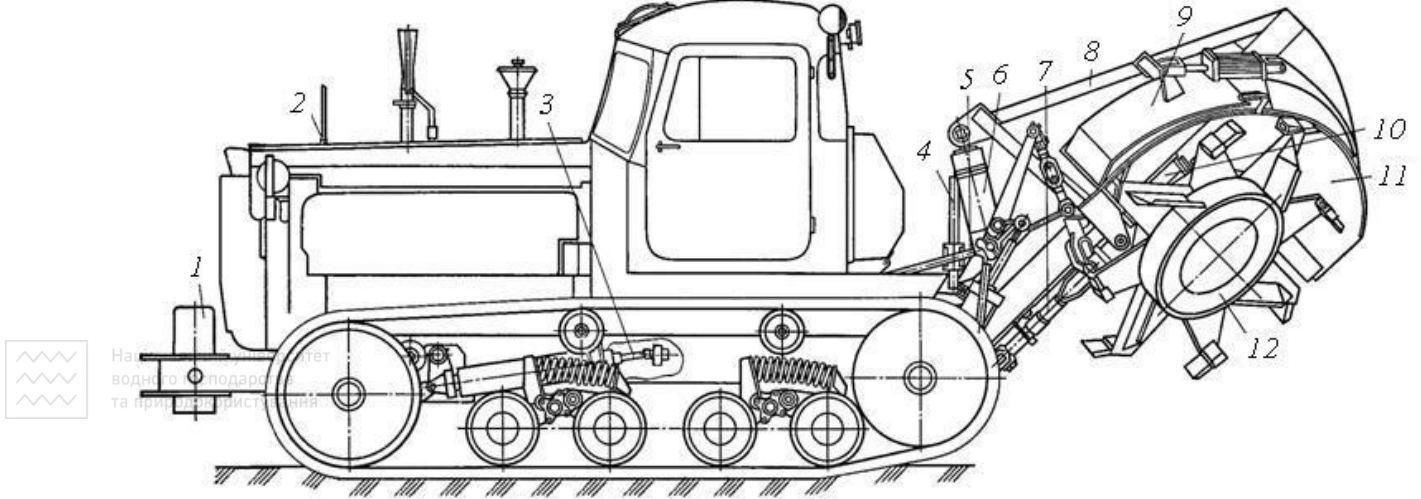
Плужнороторний каналокопач на базі гусеничного трактора:
